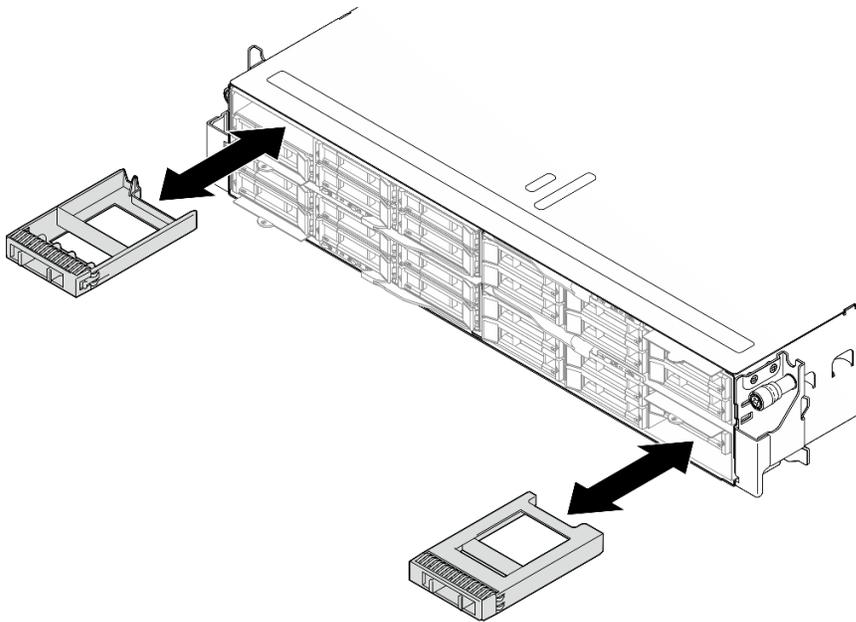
Austausch einer Abdeckblende für Laufwerke
